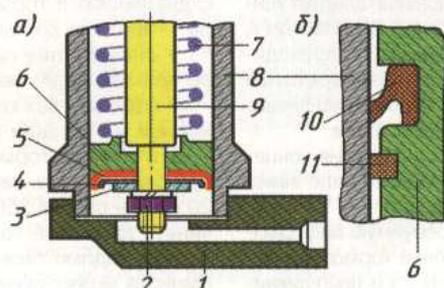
Цилиндр пневматического привода с кожаной (а) и резиновой (б) манжетами:
